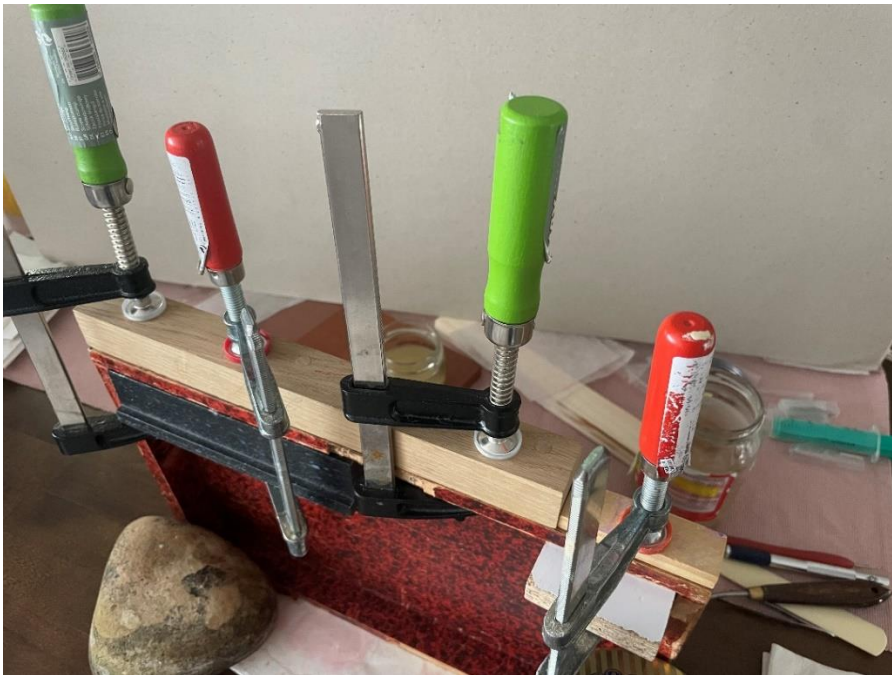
Pikema külje ühtlase surve tagamine nelja pitskruviga.
